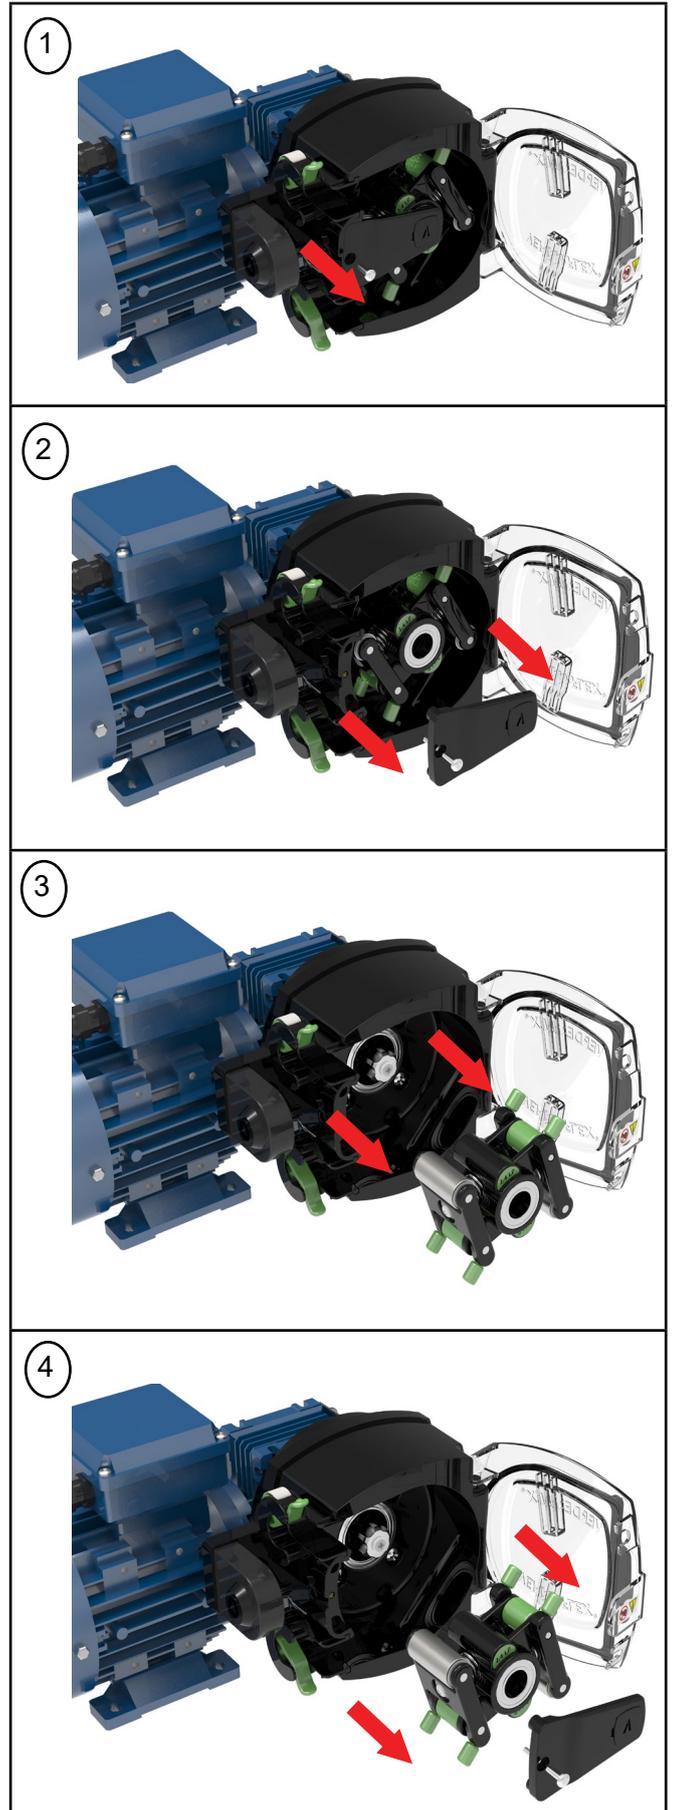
Rotorbaugruppe Ersatz - Rapide 5000
